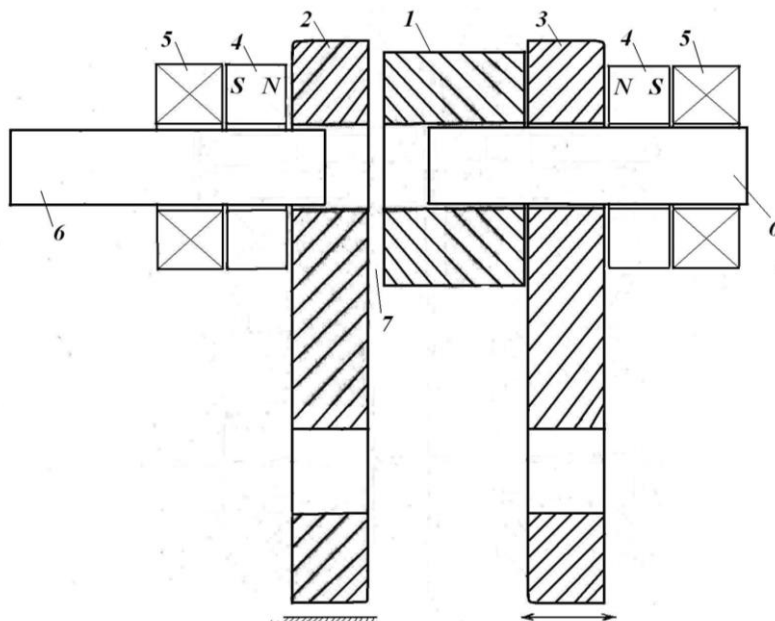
Схема з'єднань основних елементів при зварюванні щок і шийок валу:
